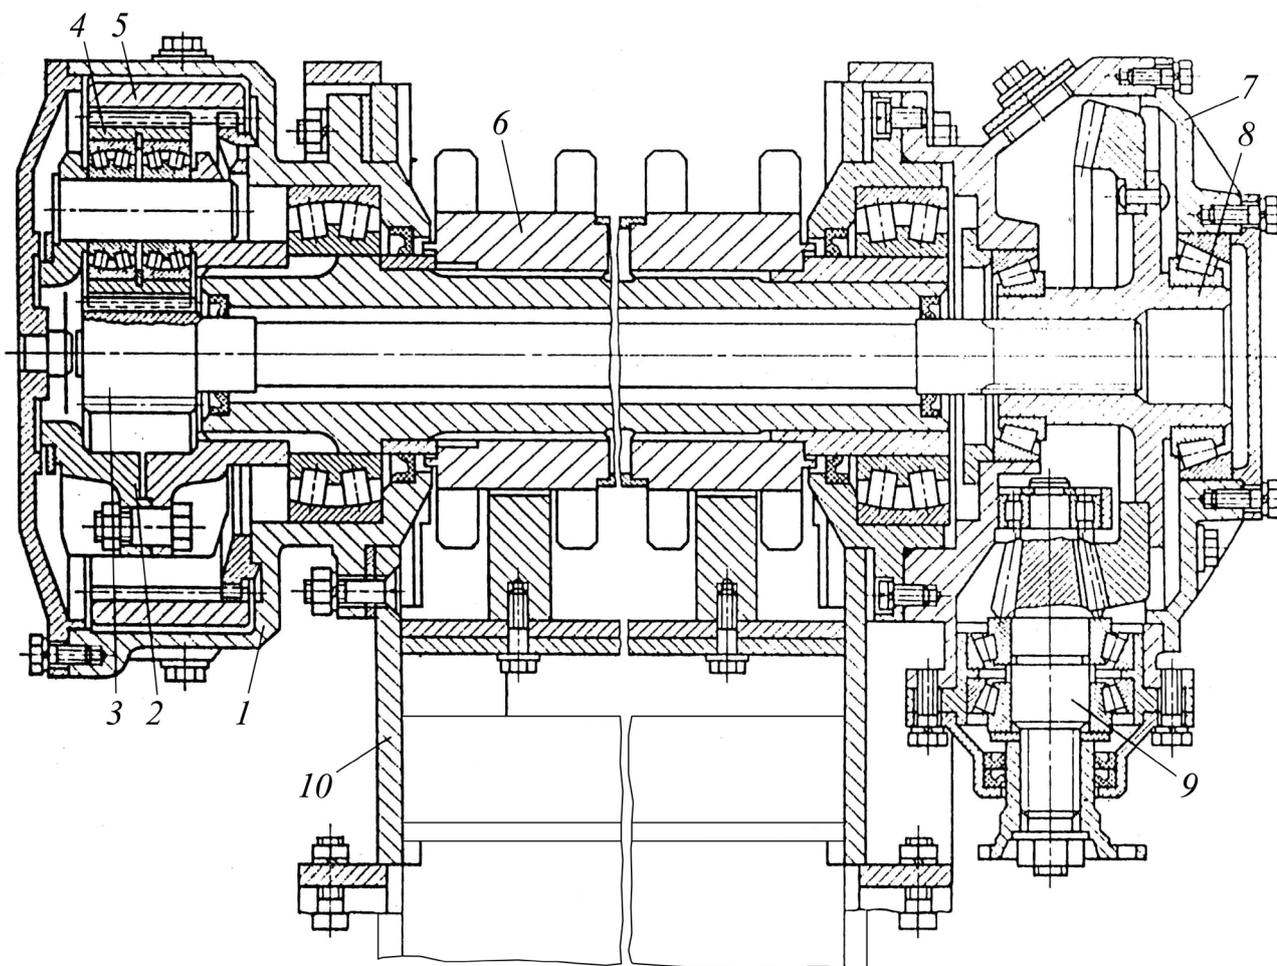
Приводная станция скребкового конвейера: 1 – корпус планетарного редуктора; 2 – водило планетарного редуктора; 3 – вал-шестерня центральная планетарного редуктора; 4 – сателлит планетарного редуктора; 5 – венец неподвижный планетарного редуктора; 6 – вал приводной скребкового конвейера; 7 – корпус конического редуктора; 8 – колесо коническое; 9 – вал-шестерня конического редуктора; 10 – рама приводной станции
